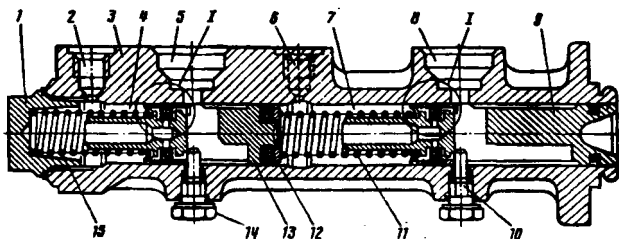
Сдвоенный главный тормозной цилиндр автомобилей ВАЗ АО "Автотаз"
